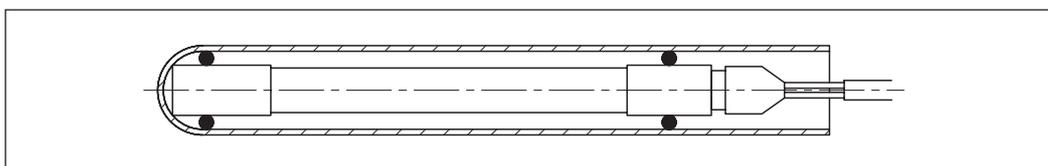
Emetteur avec joints toriques de positionnement dans le tube de protection
